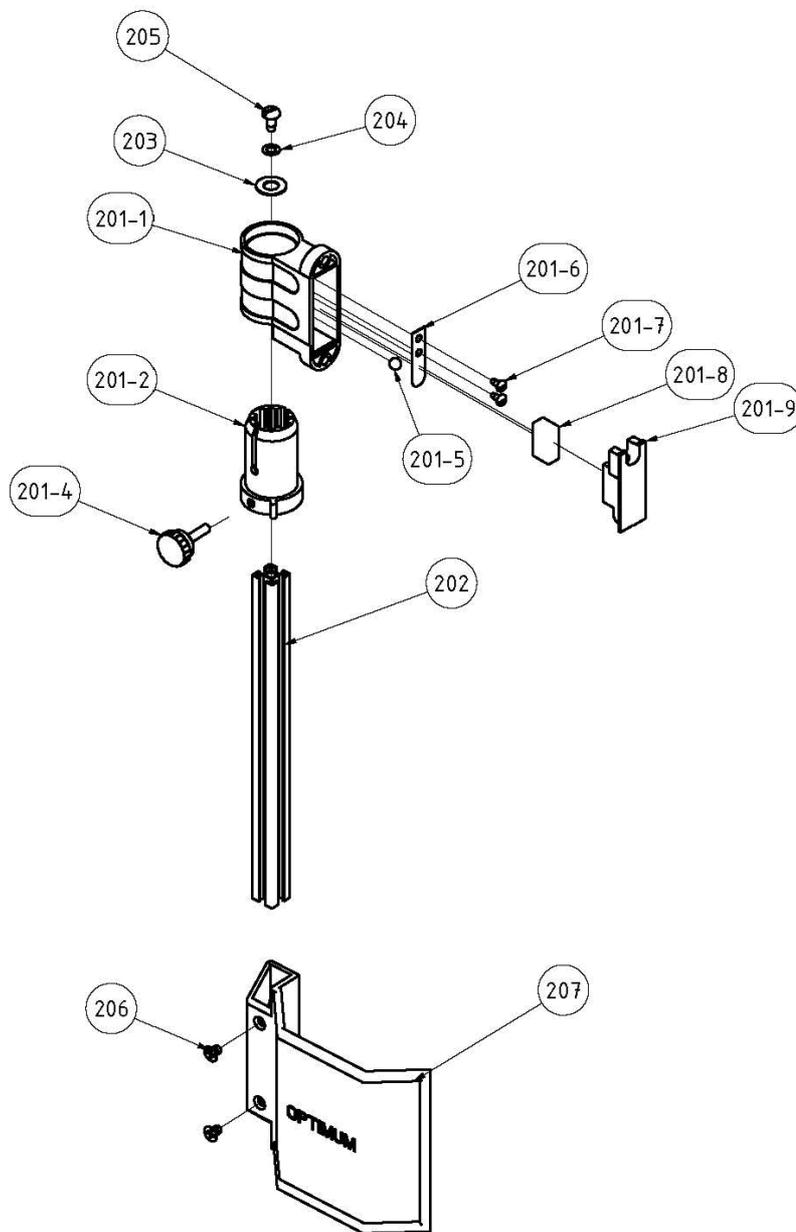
Bohrfutterschutz B17 Pro - Drill chuck protection B17 Pro
